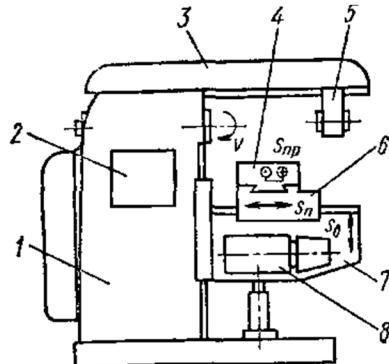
Общий вид горизонтально-фрезерного станка
